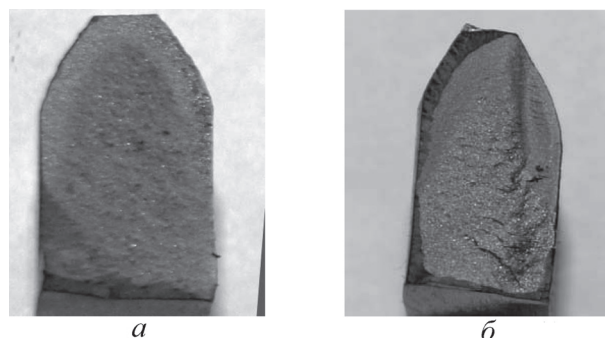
Внешний вид излома разрушенных при испытании на ударный изгиб образцов: *a* – сталь 20ХН3А; *b* – сталь 60ПП
